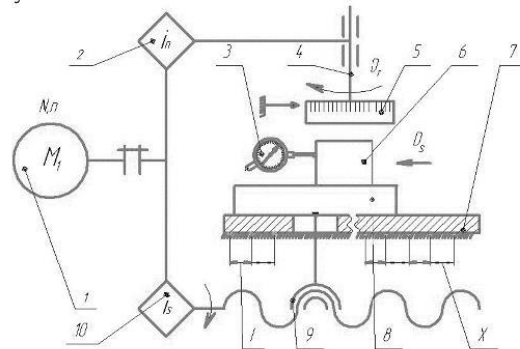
Схема вимірювання величини подачі на зуб фрези:
